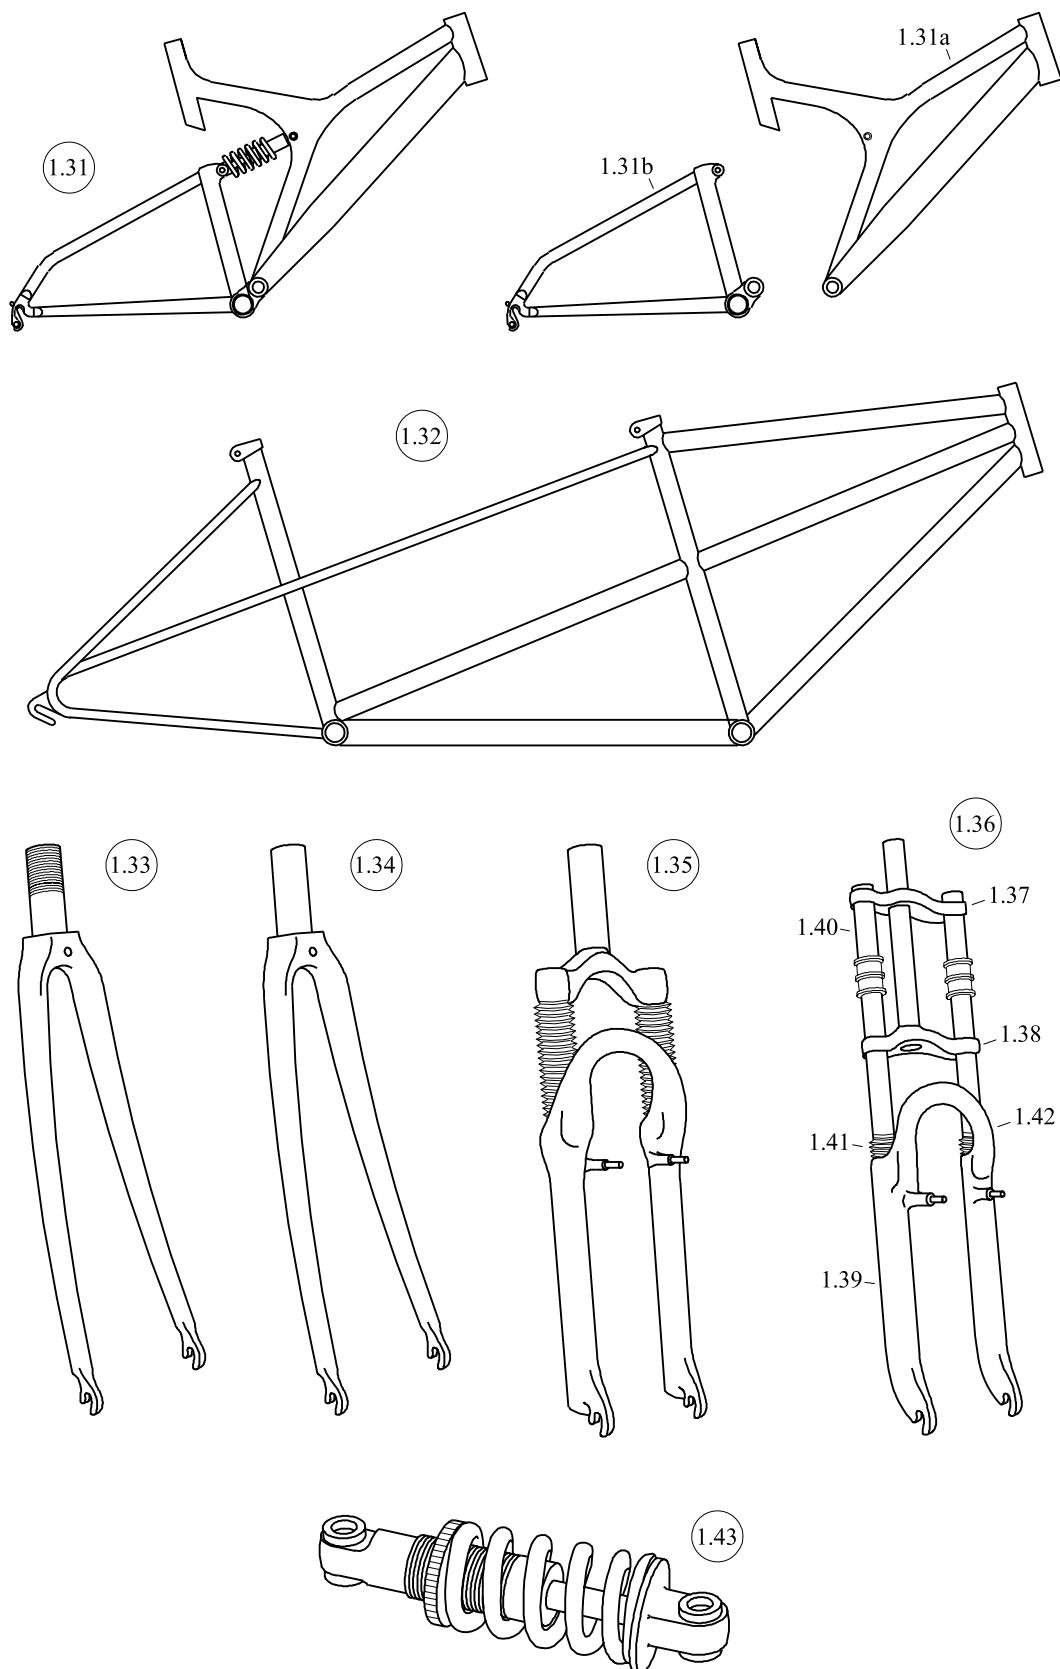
Ensemble cadre fourche / Frame fork assembly / Rahmen und Gabel / Gruppo telaio-forcella / Frame voorvork samenscholing
